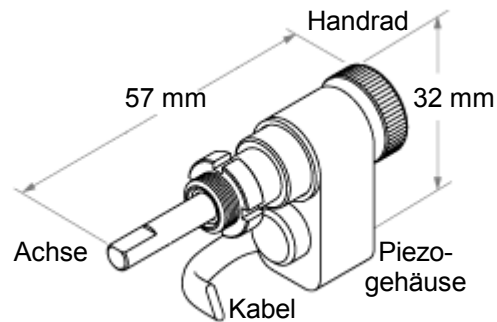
Gewindeloser Picomotor, Quelle: New Focus Inc.
